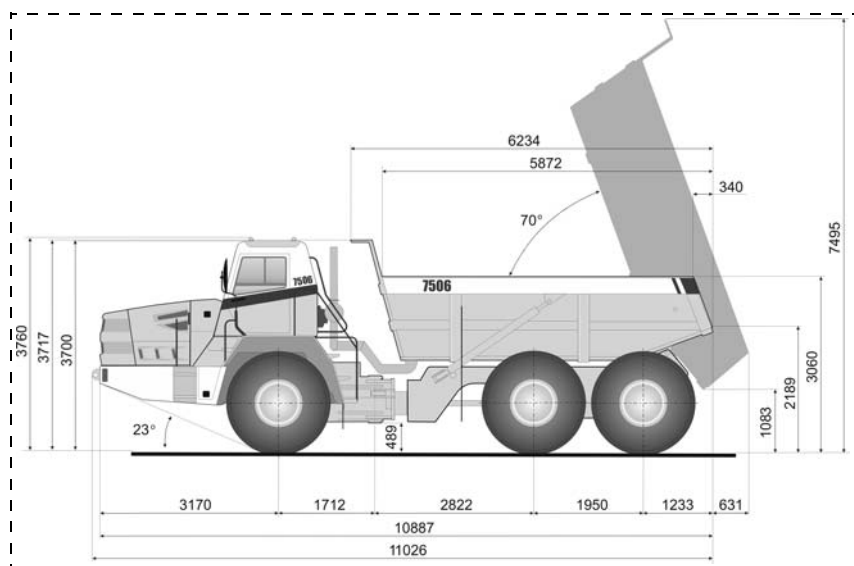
Основные размеры шарнирно-сочлененного самосвала МоАЗ-7506
